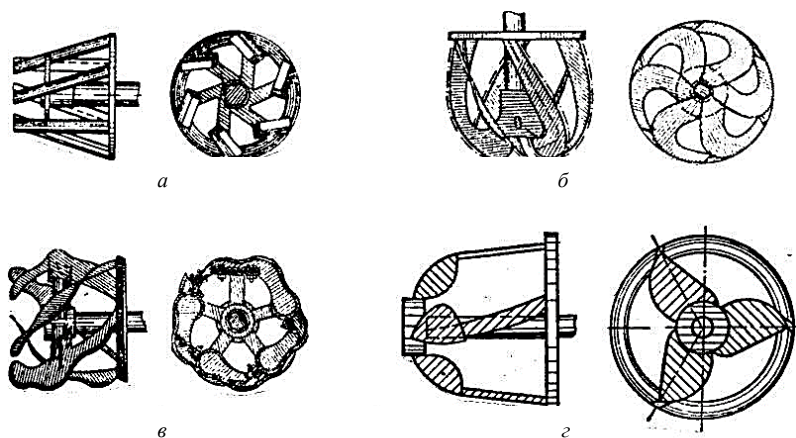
Фрезы наиболее типичных конструкций: а – открытая с плоскими ножами; б – закрытая (митрообразная) с ножами двойной кривизны; в – полуоткрытая с ножами волнообразной формы; г – с отвально-режущими лопастями
